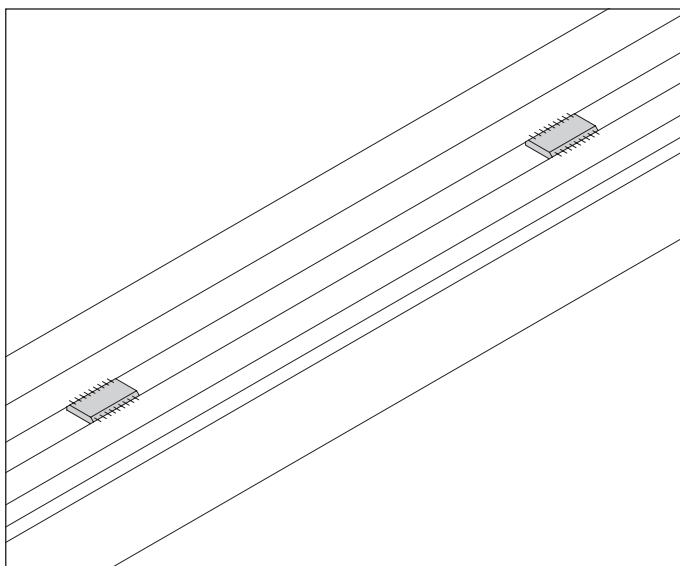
Einschweiss-Plättchen für Schlossbefestigung
